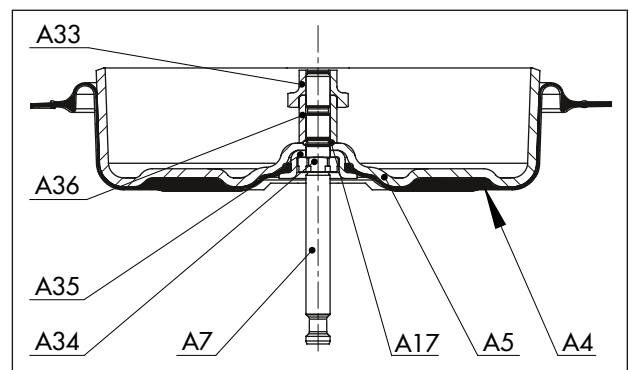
Disposición de las piezas, sentido de actuación FA (750v2 cm²)
